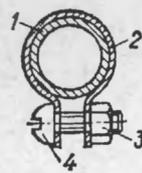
Крепление защитного хомутка на вилку заднего колеса (сечение К—К на рис. 58):
